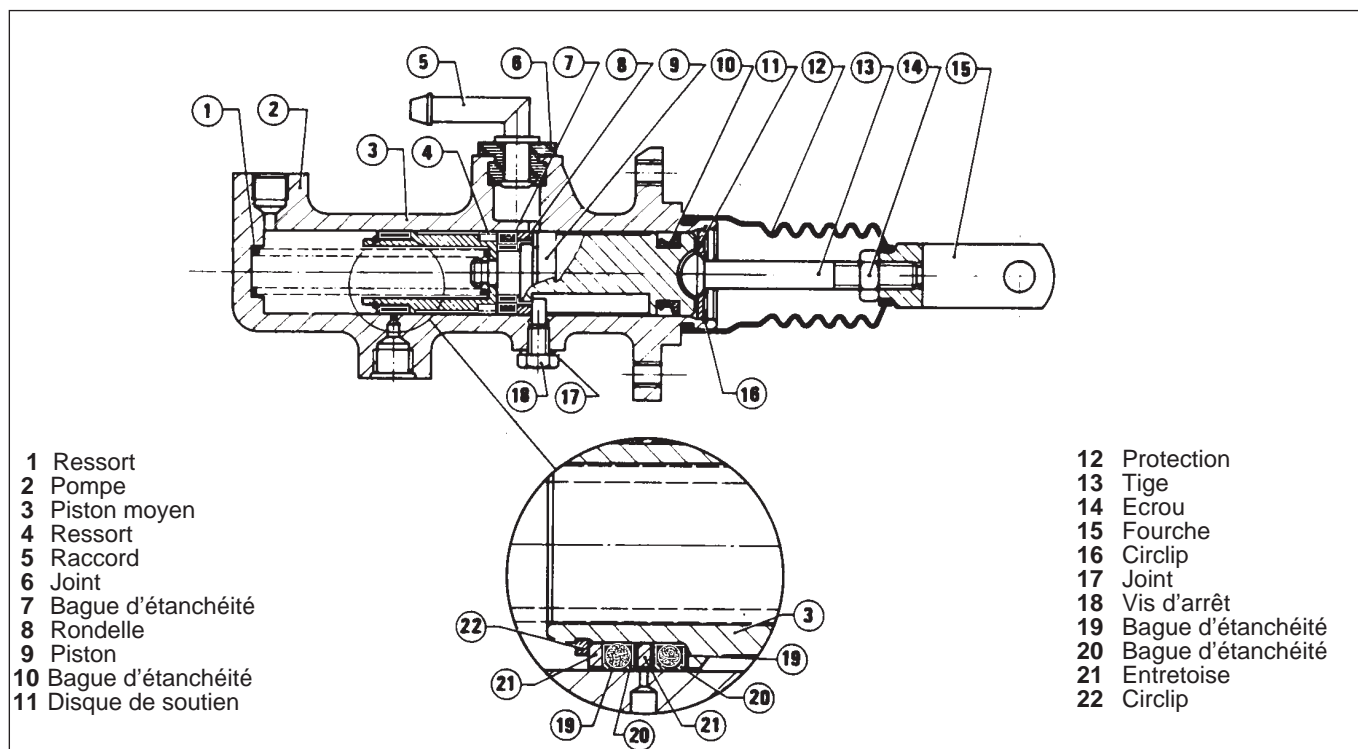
Vue en coupe de l'ensemble de pompe de freins.
